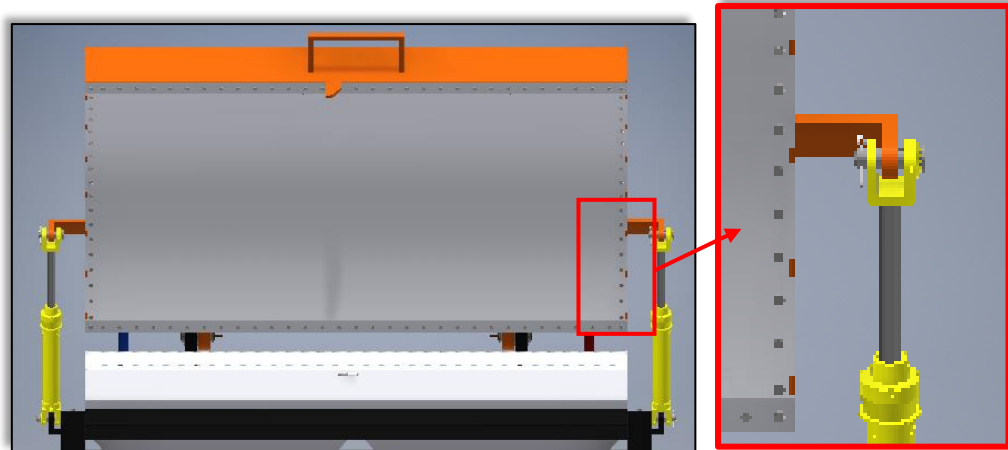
Separación desfavorable de cilindros a plato y estructura.
